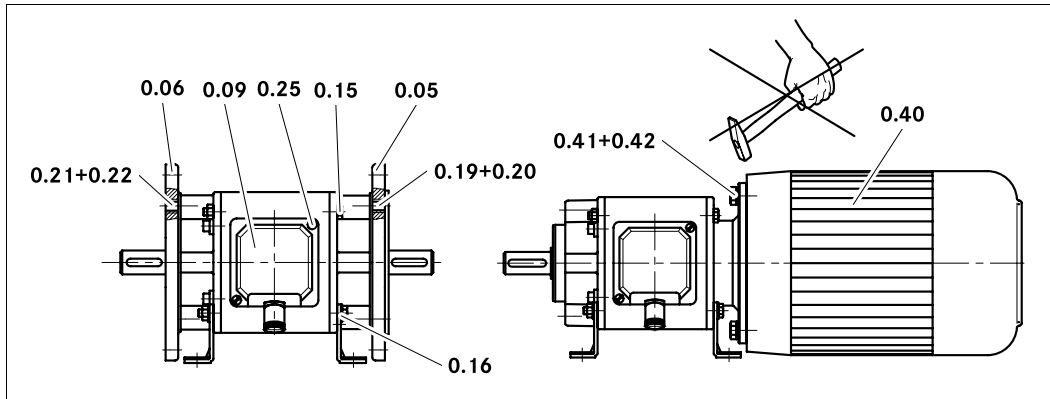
Ausführung; 14.800.□□.13.2(7)
